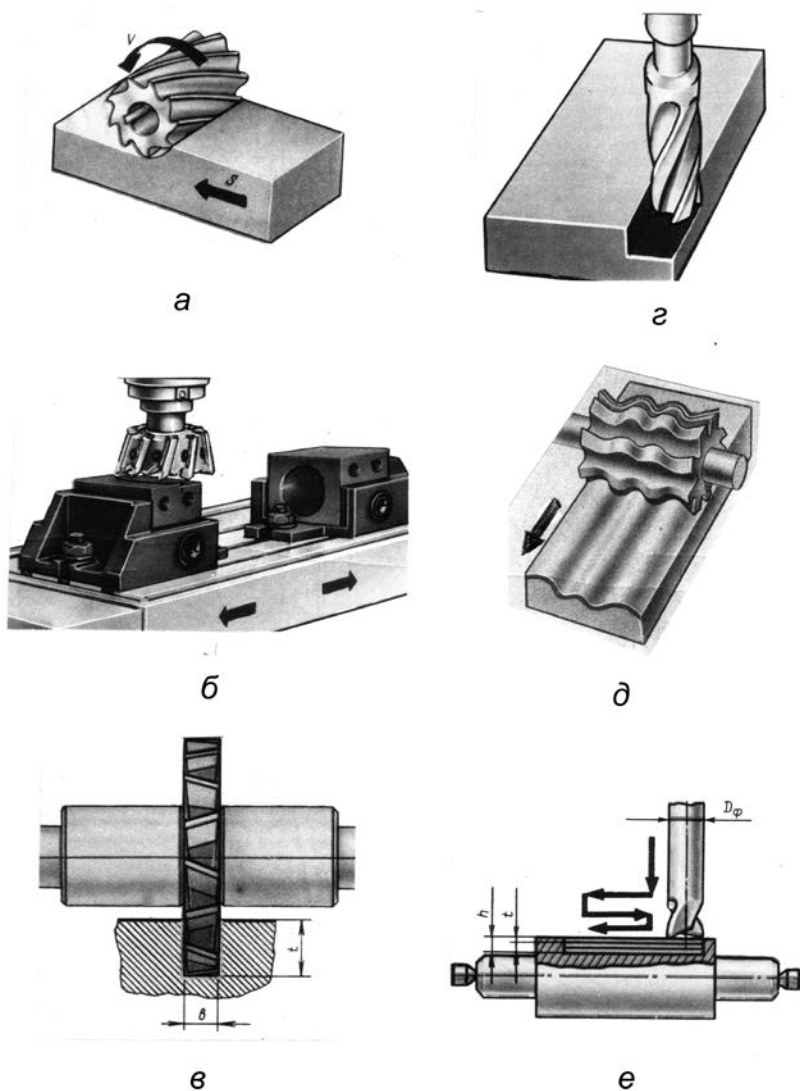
Обработка типовых поверхностей разными видами фрез:
